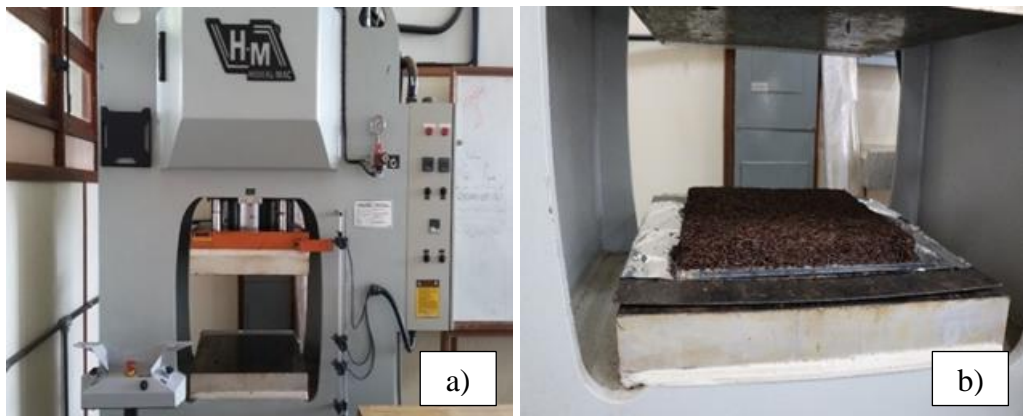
Moldagem dos painéis: a) Prensa hidráulica HIDRAL-MAC, b) Material posicionado para prensagem.
